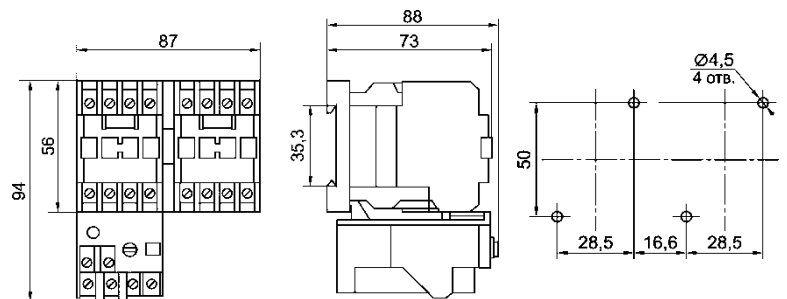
Пускатель реверсивный ПМ12-010 10А. Степень защиты - IP00; IP20.
